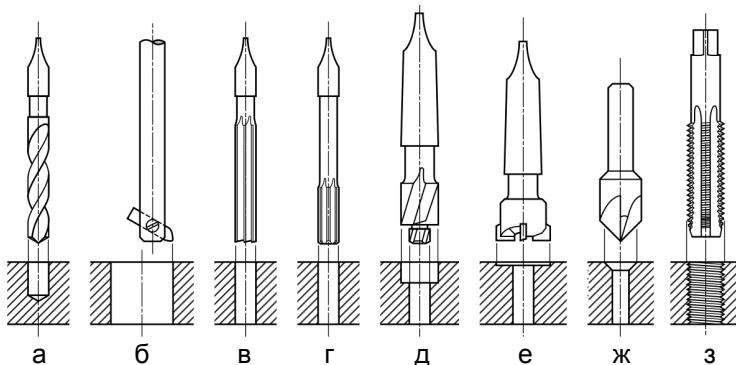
Схеми обробки отворів: а – свердління; б – розточування на токарному верстаті (борштанга); в – зенкерування; г – розвертання; д, е – цекування; ж – зенкування; з – нарізання різьблення митчиком
